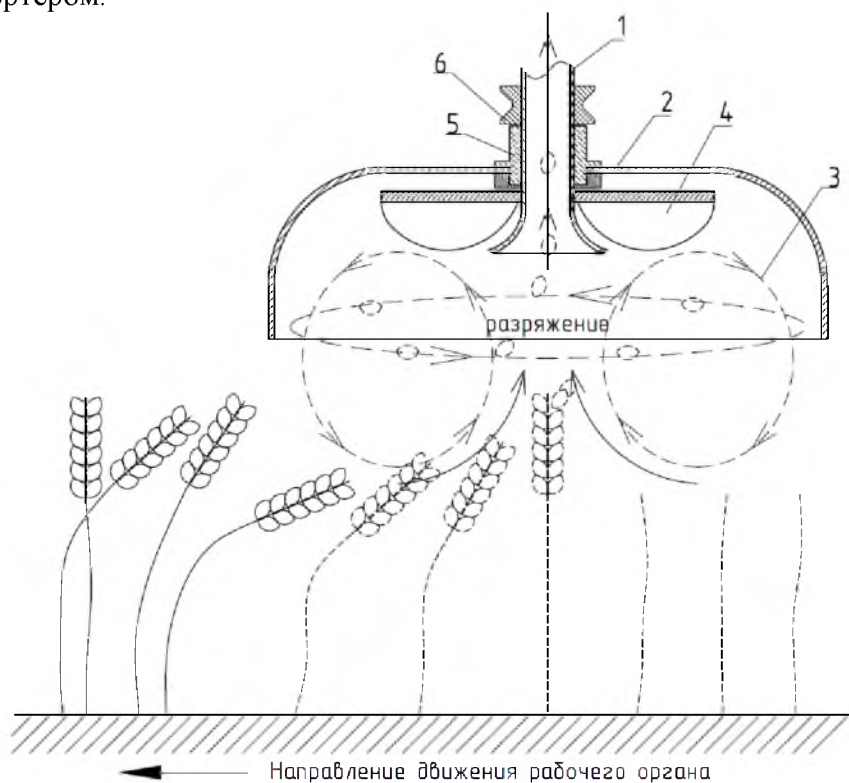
Устройство и принцип действия рабочего органа тороидальной жатки:
